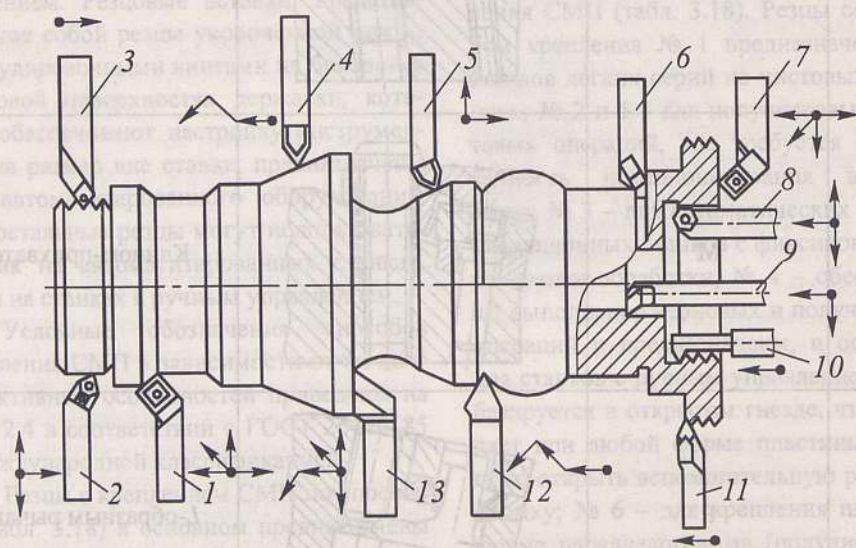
Схема обработки основных типовых поверхностей токарными резцами: 1, 2, 7 – проходные резцы; 4, 5, 12, 13 – контурные резцы; 3, 10, 11 – резцовые резцы; 8, 9 – расточные резцы; 6 – канавочный резец
